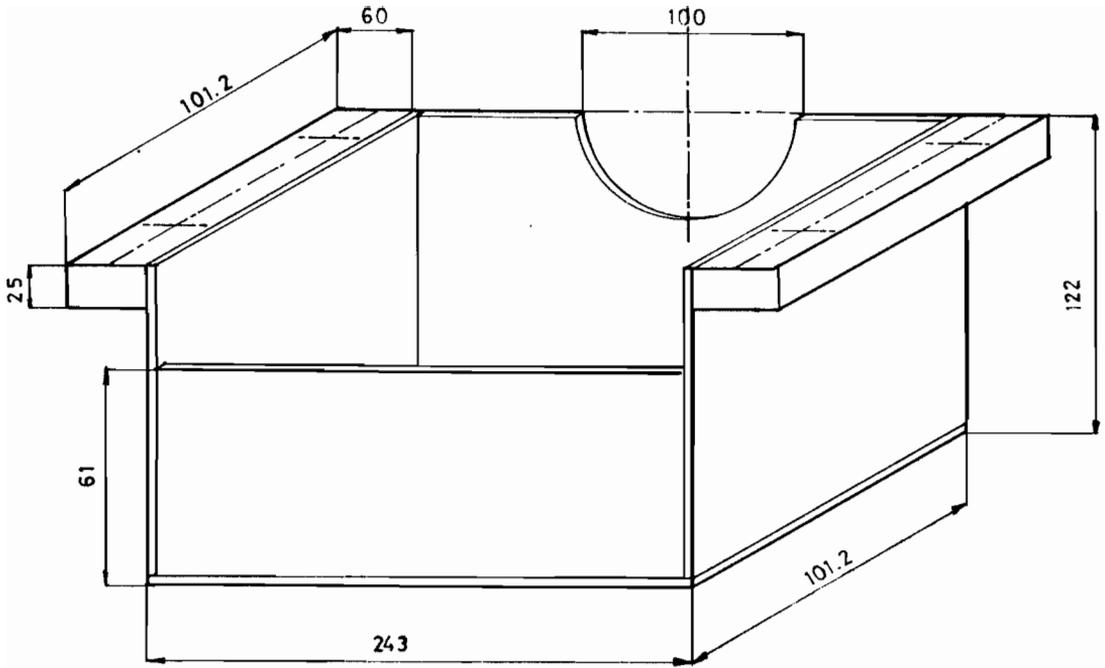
DIMENSIONES DE LA CANASTILLA (PERNOS DE 9/16").
